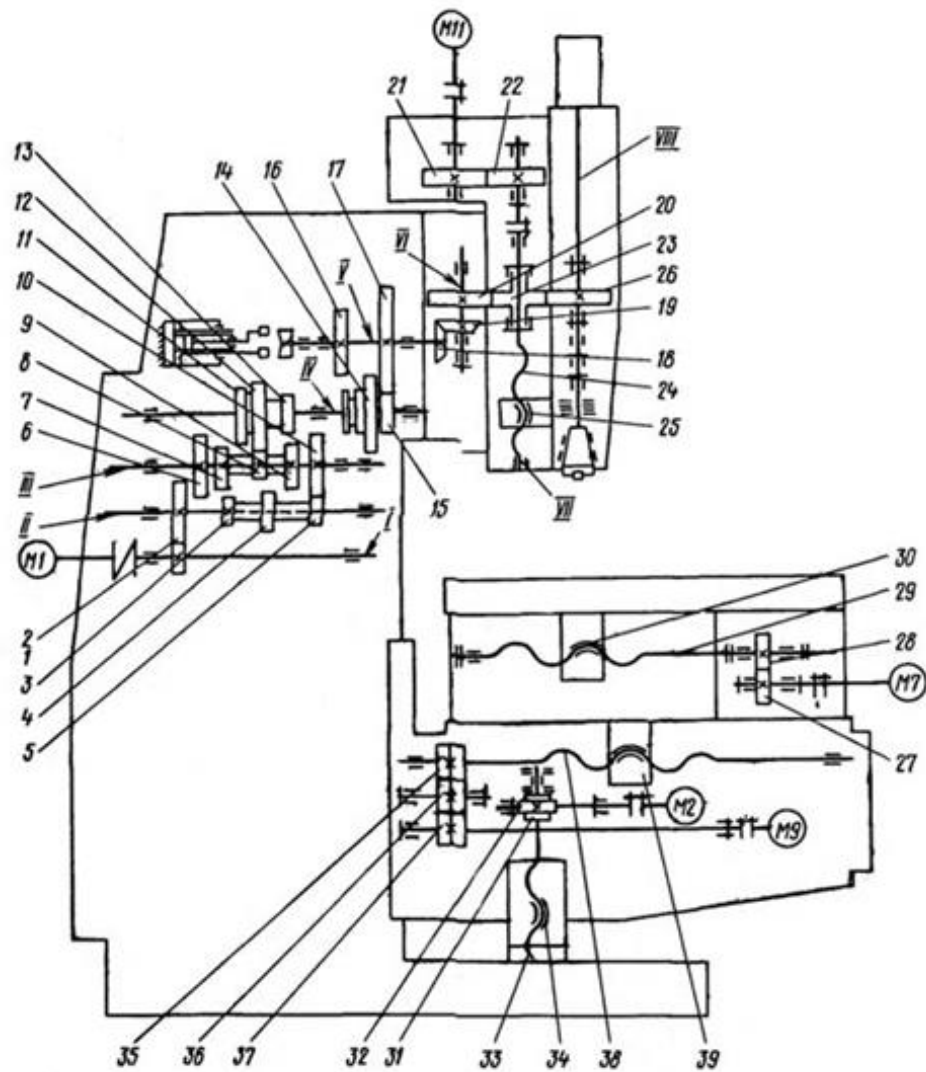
Кинематическая схема консольно-фрезерного станка ГФ2171
